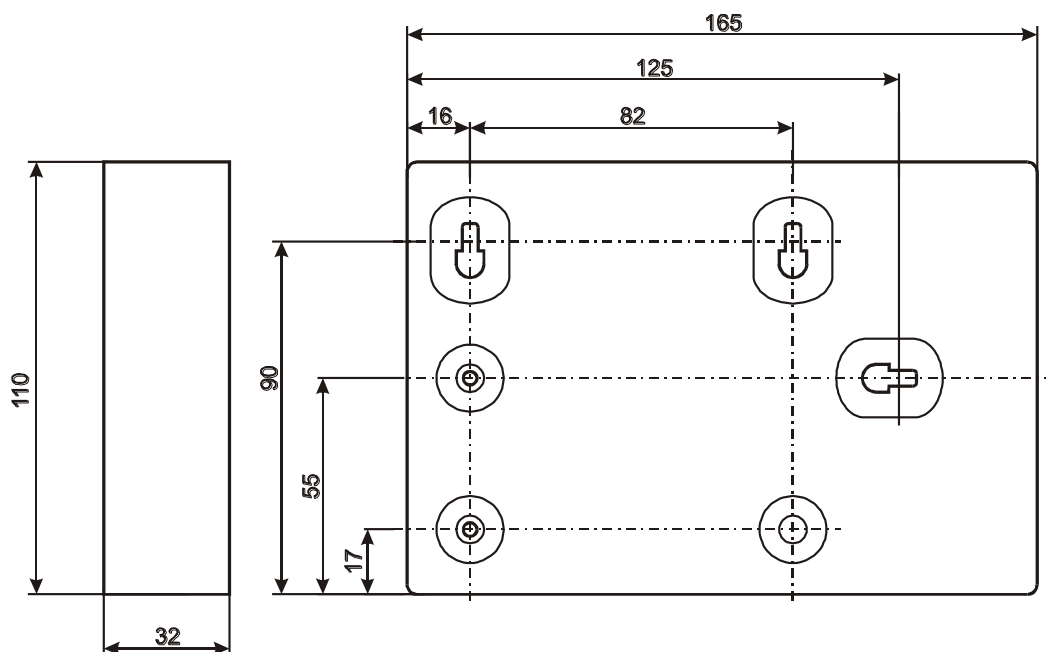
Внешний вид и габаритные размеры БРЛ в исп. IP20
